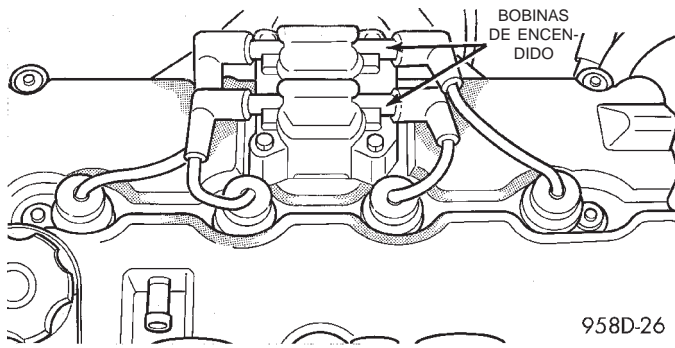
Conjunto de bobina de encendido — Motor 2.4L
